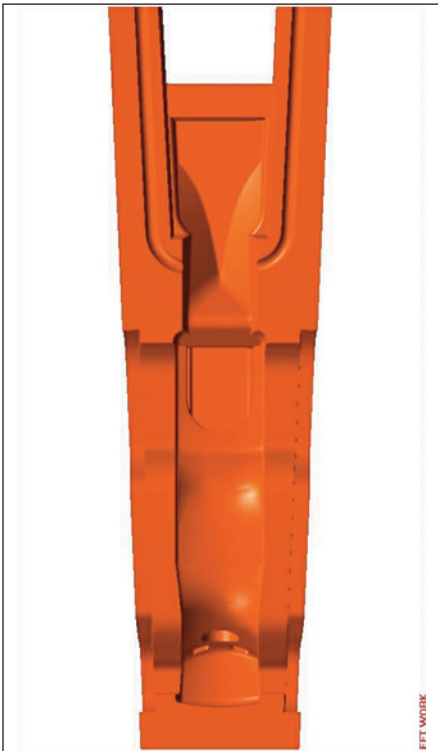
Formendesign für das Schweißverfahren SkV-Elite (Sicht auf die Innenseite der Form)
